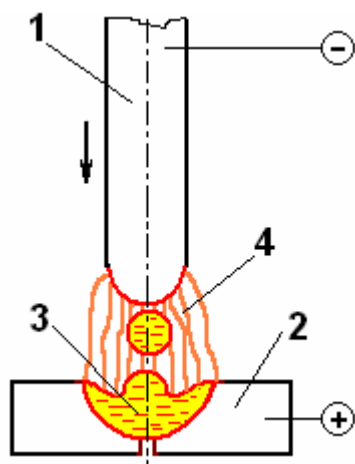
Схема сварочной дуги постоянного тока:
